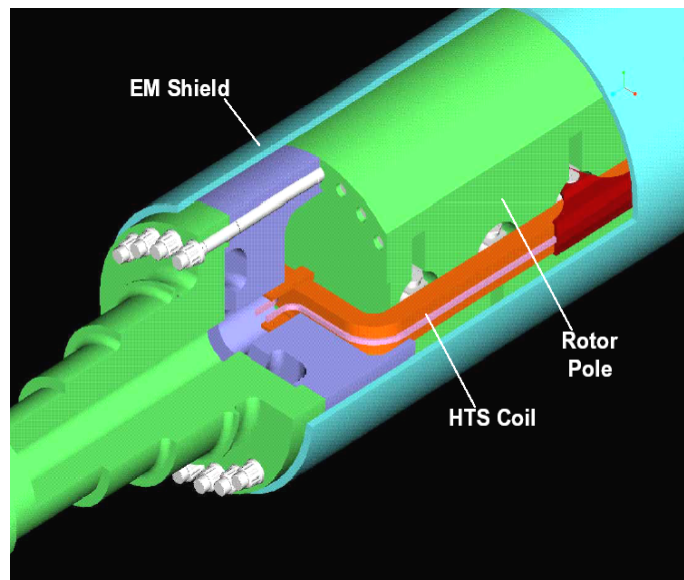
HTSL-Rotor zum 100MVA-Generator mit magnetischem Rotorkern, Quelle [10]
